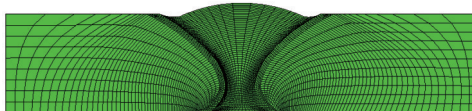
激光-电弧复合焊接 7020-T651 铝合金的完整接头网格模型
